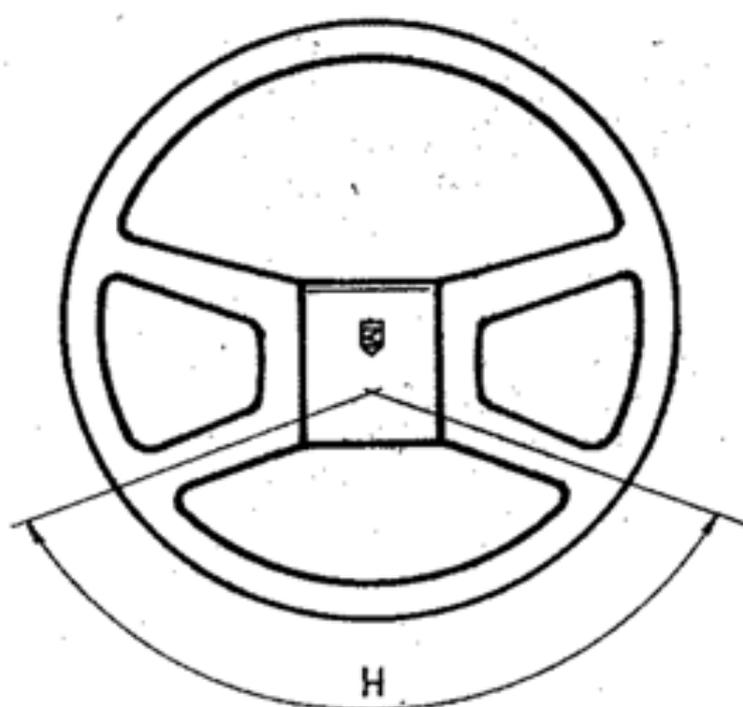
Рулевое колесо автомобиля ЗАЗ-110216, "Люкс".
